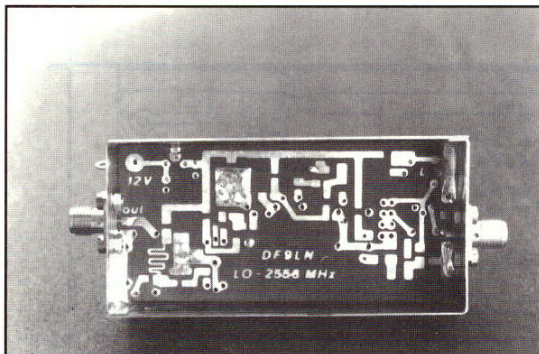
Preparazione per il montaggio: prima del montaggio componenti SMD, i bordi del PCB vengono saldati alle pareti della scatola. Si saldano tutti i ritorni a massa fra piste e superficie opposta tutto rame. Dopo lavaggio con trielina si montano e si saldano gli spilli degli SMA.
